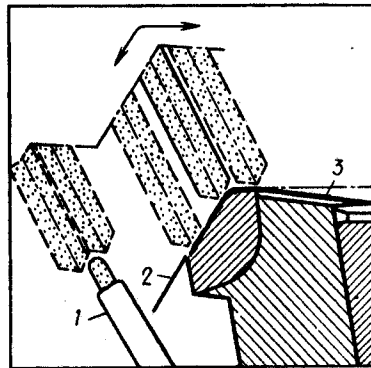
Схема копирной контурной заточки ножа торцовой фрезы: 1 — алмаз в оправке для правки круга, 2, 3 — главная и вспомогательная режущие кромки
